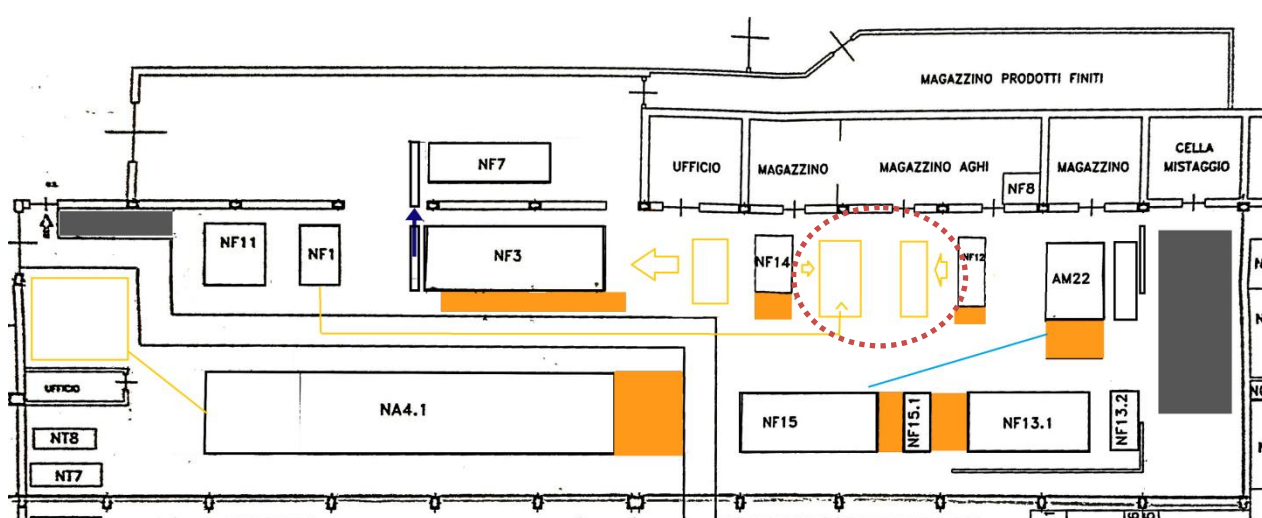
nuovo layout con i buffer e la postazione per un addetto all'imballaggio.
